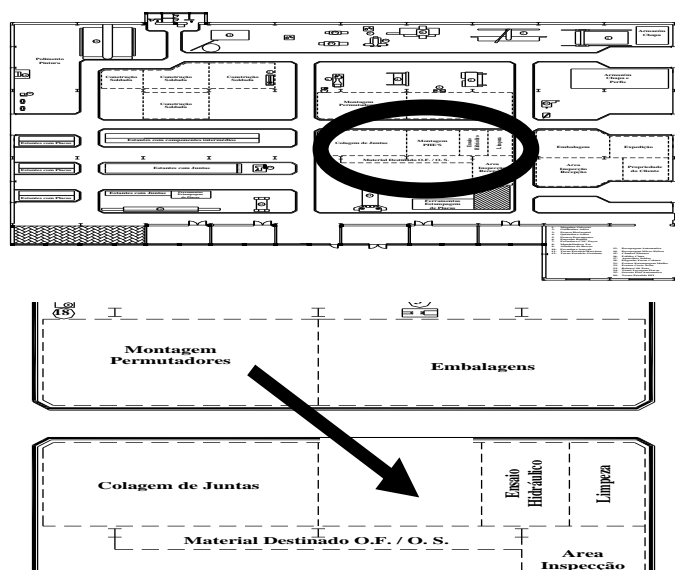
5 Mudança do *Layout* da secção da Montagem
